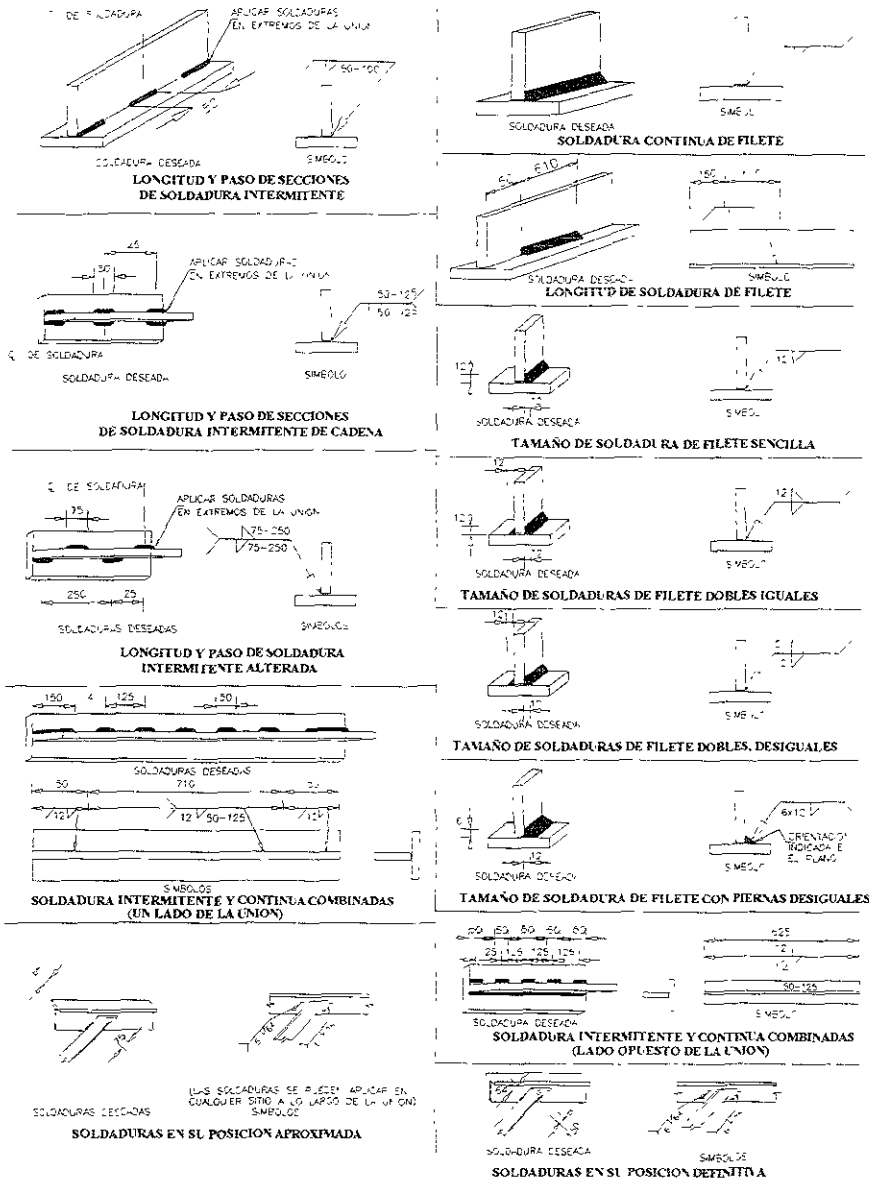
Ejemplos típicos de símbolos para soldaduras de filete
